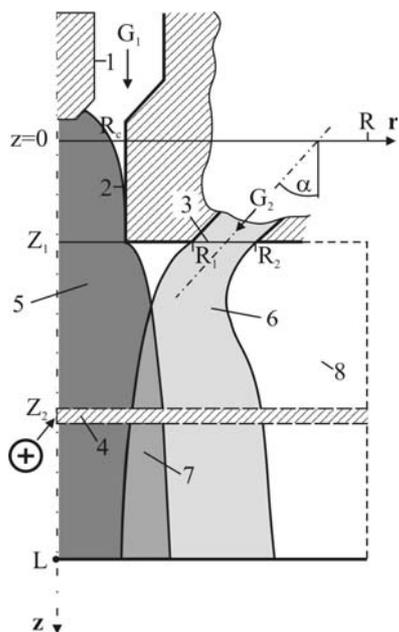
Схема плазменно-дугового металлатора: 1 – катод; 2 – сопло металлатора, 3 – канал подачи обдувающего газа; 4 – проволока-анод; 5 – плазма; 6 – газ обдувки; 7 – плазменная смесь; 8 – окружающая среда
